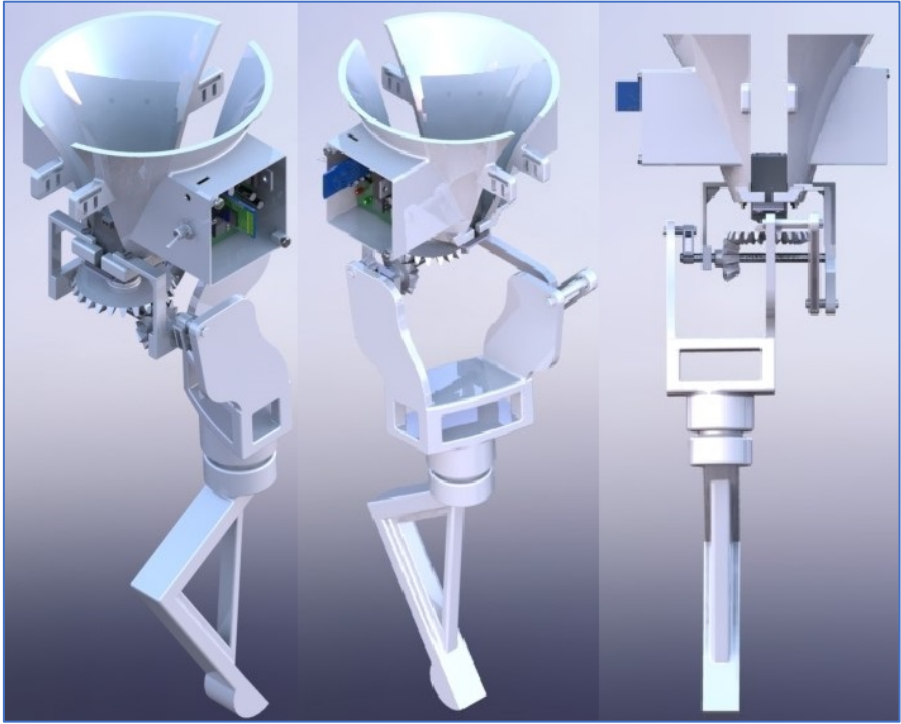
a) Ensamble CAD del prototipo de prótesis
